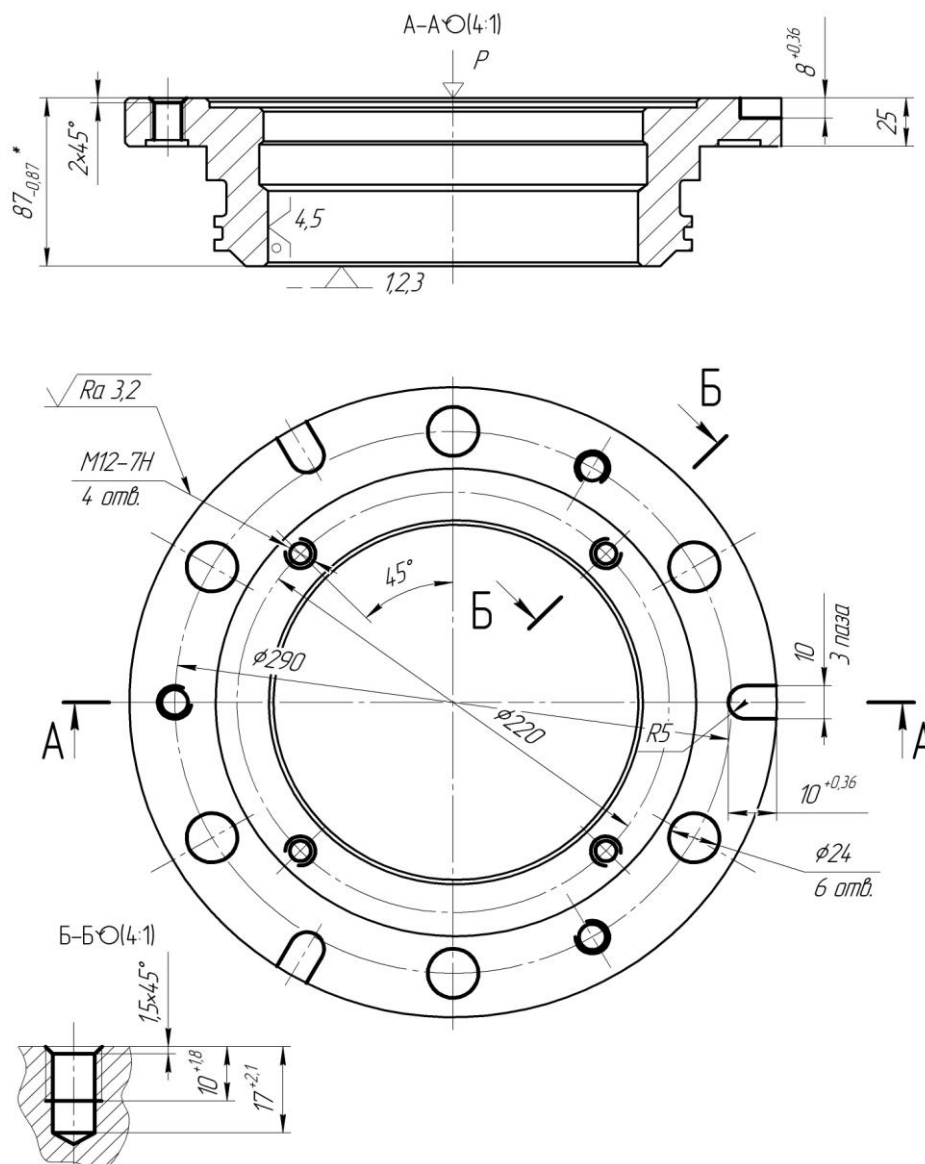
Схема базирования заготовки на вертикально-фрезерной с ЧПУ операции (первый вариант)
